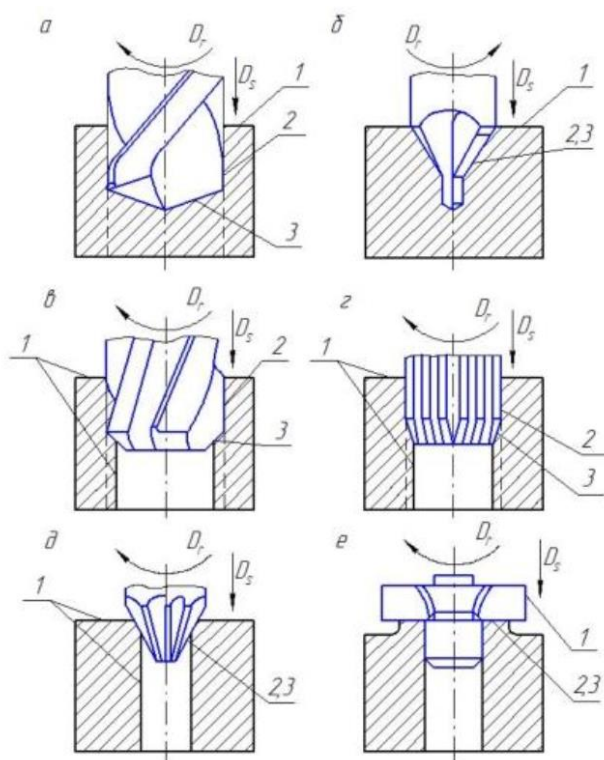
Схемы видов лезвийной обработки: а - сверление; б - центрование; в - зенкерование; г - развертывание; д - зенкование; е - цекование; 1 - обрабатываемая поверхность; 2 - обработанная поверхность; 3 - поверхность резания;  $D_r$  - главное движение;  $D_s$  - движение подачи.
